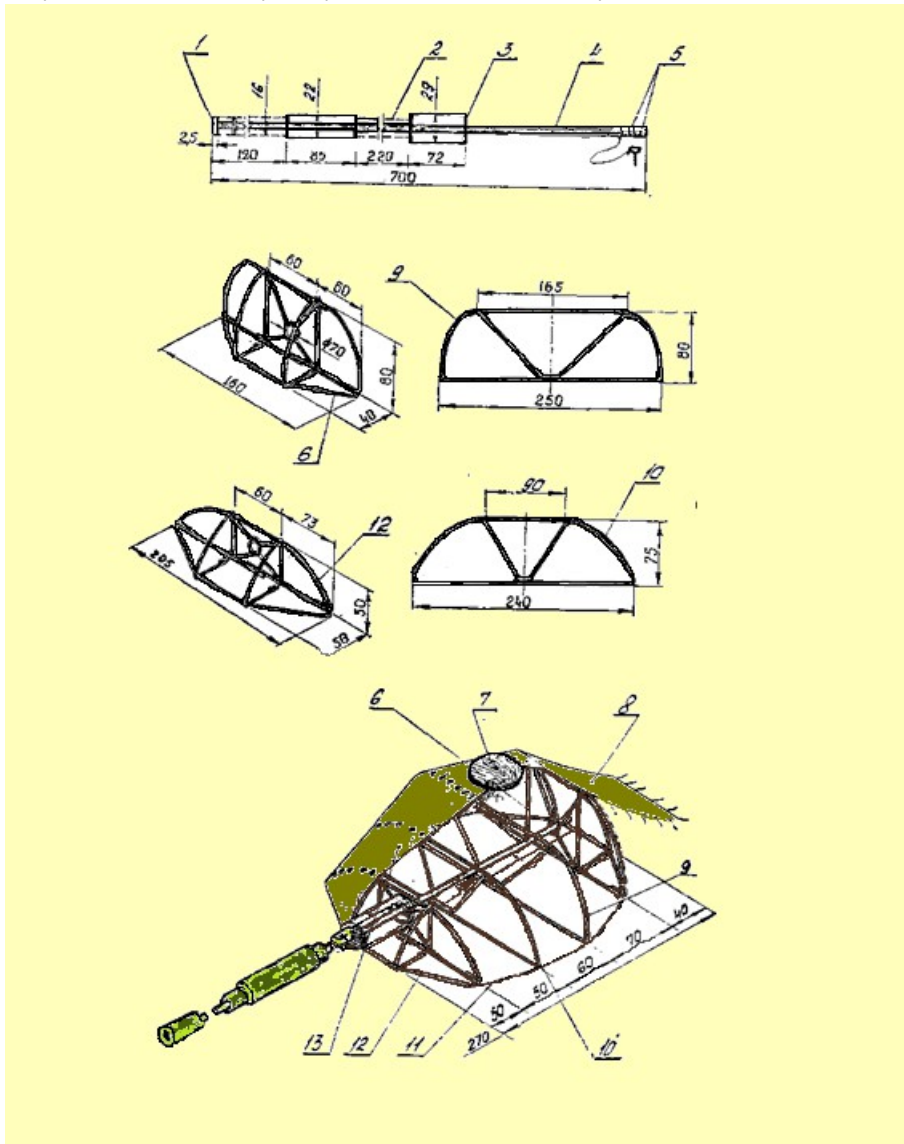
Макет башни танка, изготовленный из круглой стали и ткани
